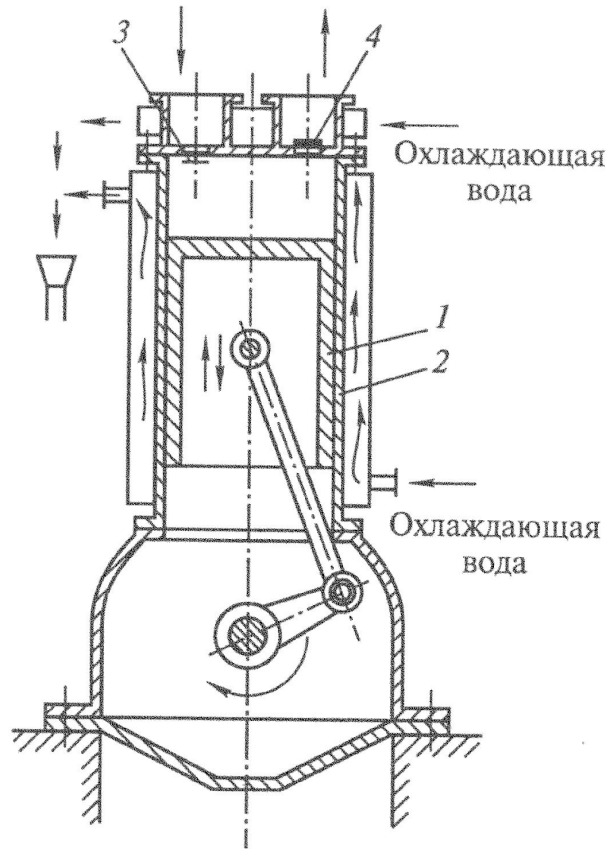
Схема поршневого компрессора с одной ступенью сжатия: 1 — поршень; 2 — цилиндр; 3, 4 — всасывающий и нагнетательный клапаны
